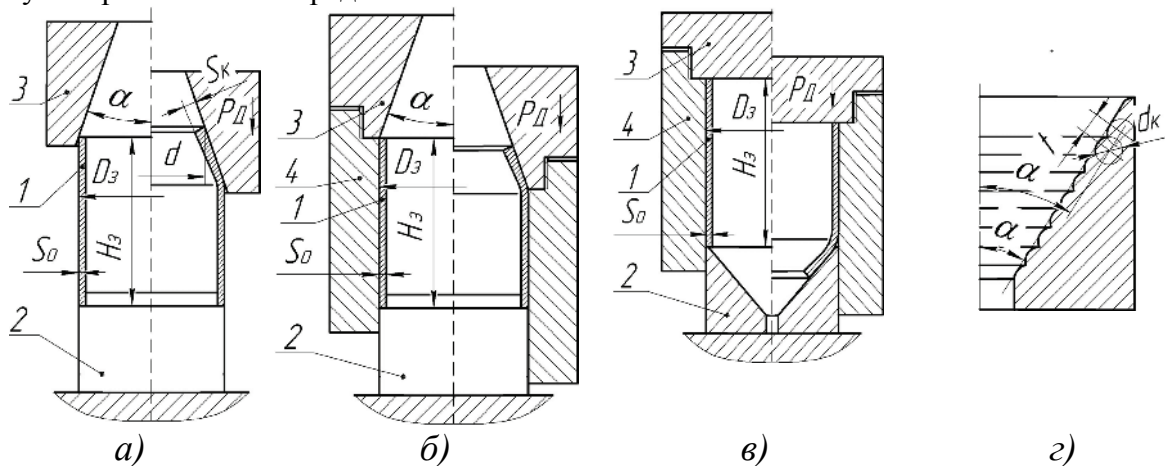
Способи обтиску трубчастих заготовок в традиційній конусній матриці
